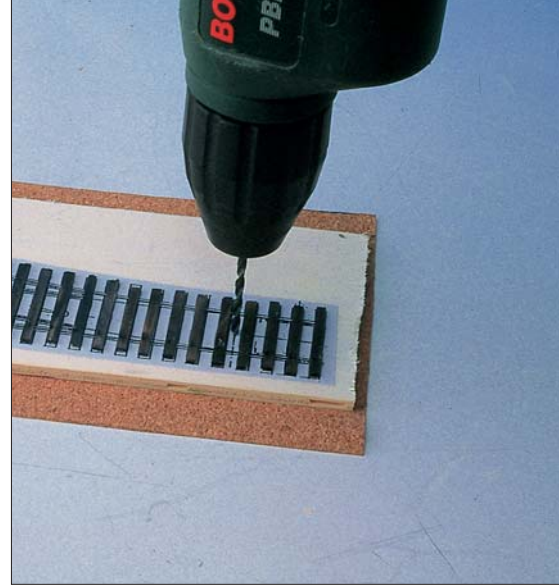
Die Öffnung für den Stelldraht wird gebohrt.
